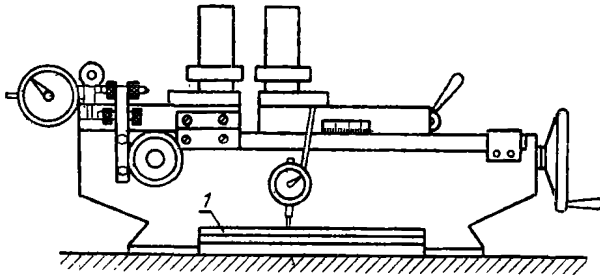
Установка поворачивающей линейки и державки с индикатором
